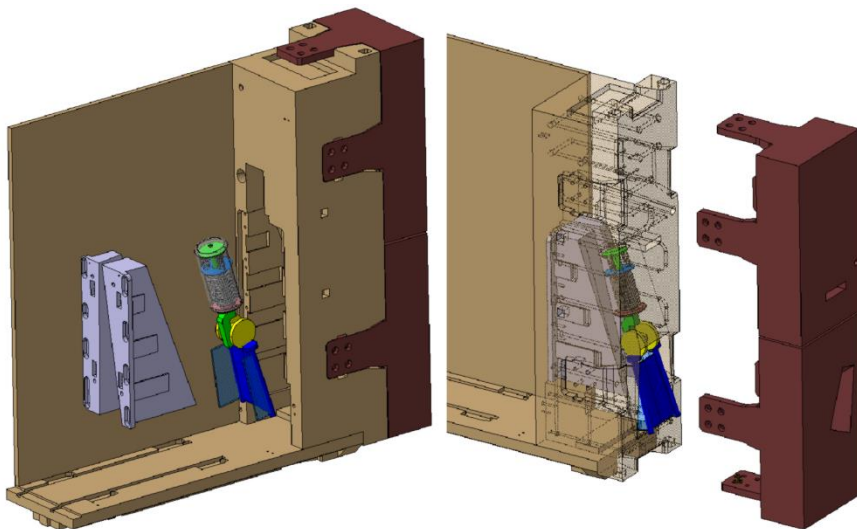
Detalhe do montagem do shutter (fonte: Active Space Technologies).
